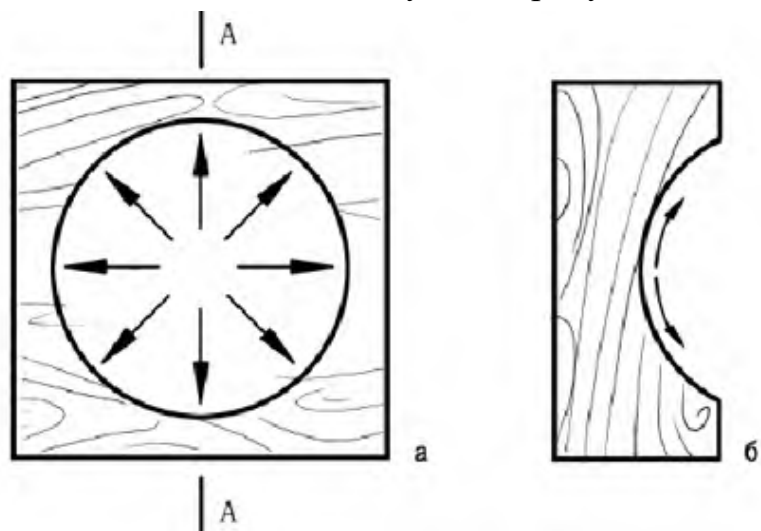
Выполнение круглой вогнутой выемки на торце заготовки вторым способом (стрелками показано направление движения инструмента)
